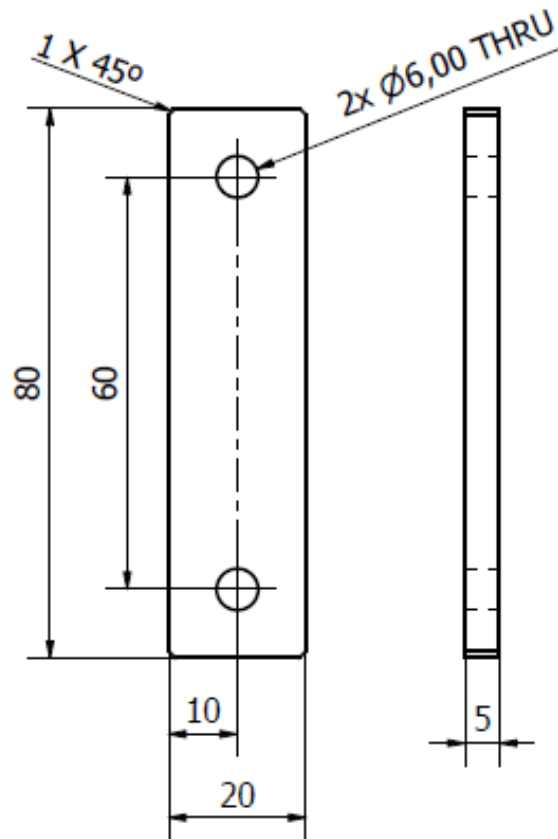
Exemplo de desenho 2D de um paralelepípedo simples
